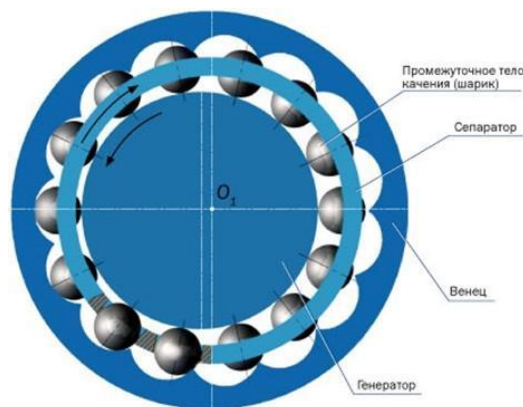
Конструкция волнового редуктора с промежуточными телами качения
